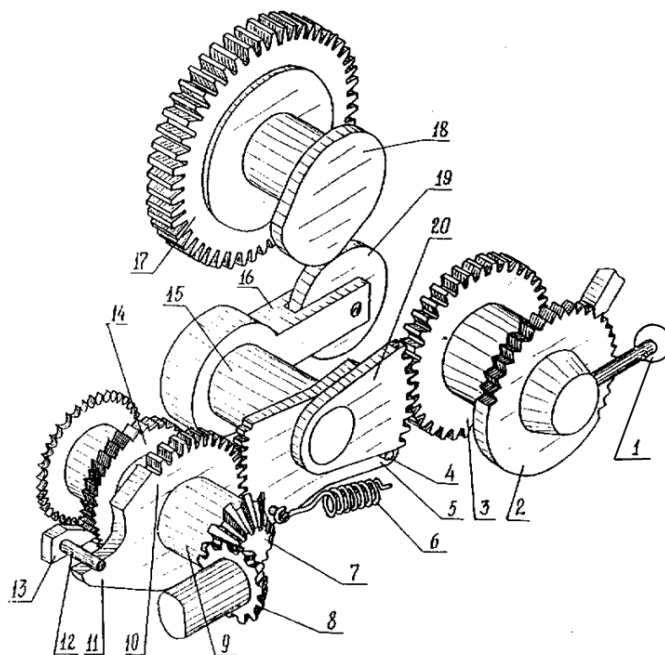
Механизм подачи: 1 – рукоятка; 2 – корпус; 3 – зубчатое колесо; 4 – штифт; 5 – зубчатый сектор; 6 – пружина; 7, 8 – конические зубчатые колеса; 9 – вал; 10 – зубчатый сектор; 11 – поводок; 12 – ось; 13 – собачка; 14 – храповое колесо; 15 – валик; 16 – рычаг; 17 – кулисный барабан; 18 – эксцентрик; 19 – ролик; 20 – зубчатый сектор
